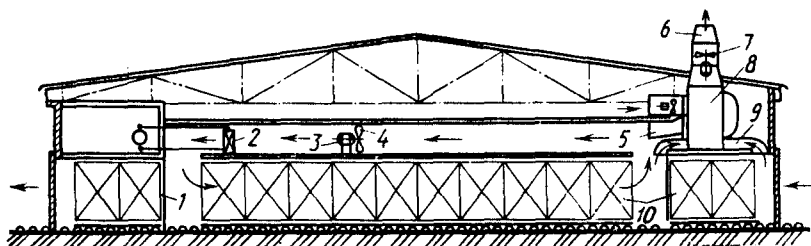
Сборная камера непрерывного действия СП-5КМ:
